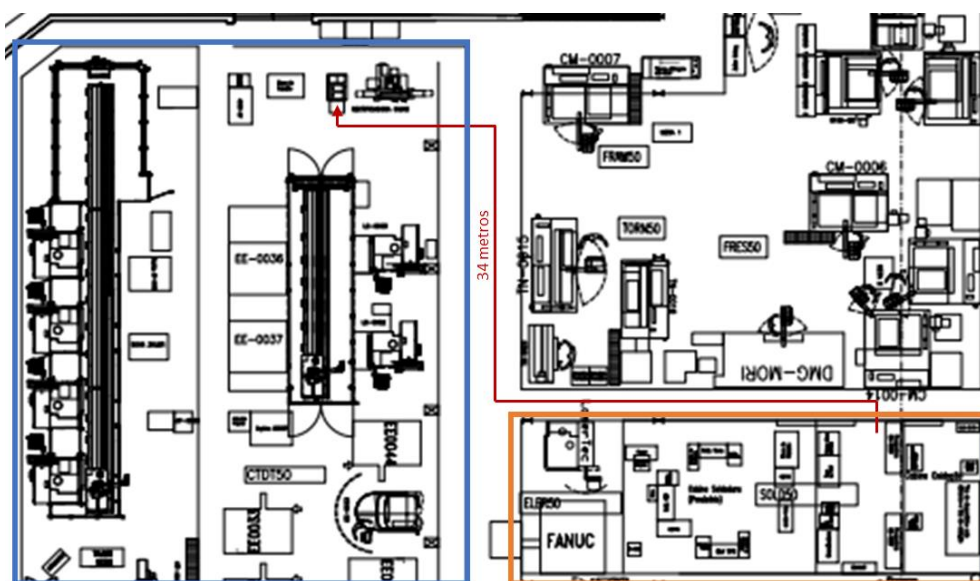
Distância percorrida desde o centro de soldadura até à máquina de medição presente no CTDT
